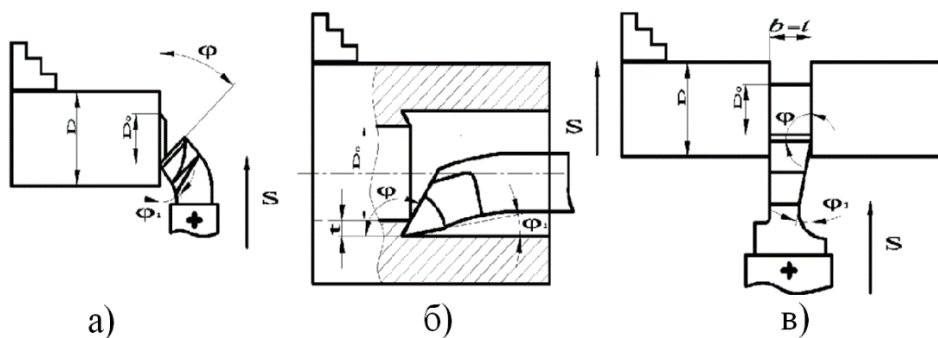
Токарні різці: а – підрізний; б – розточувальний; в – відрізний
